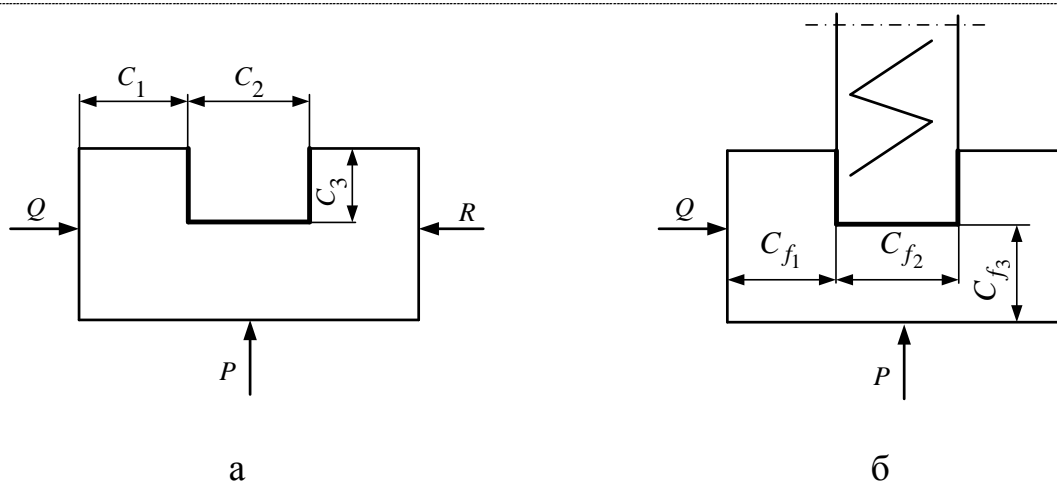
Эскиз детали и схема наладки при обработке канавки:
